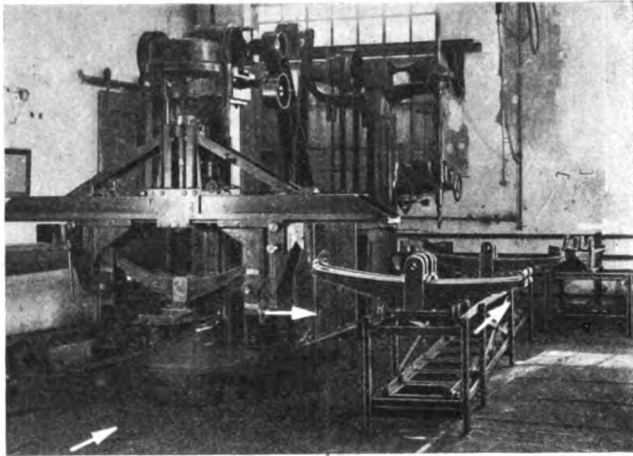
Federprüfmaschine und Bohrmaschine zum Bearbeiten der Federbolzenlöcher.
